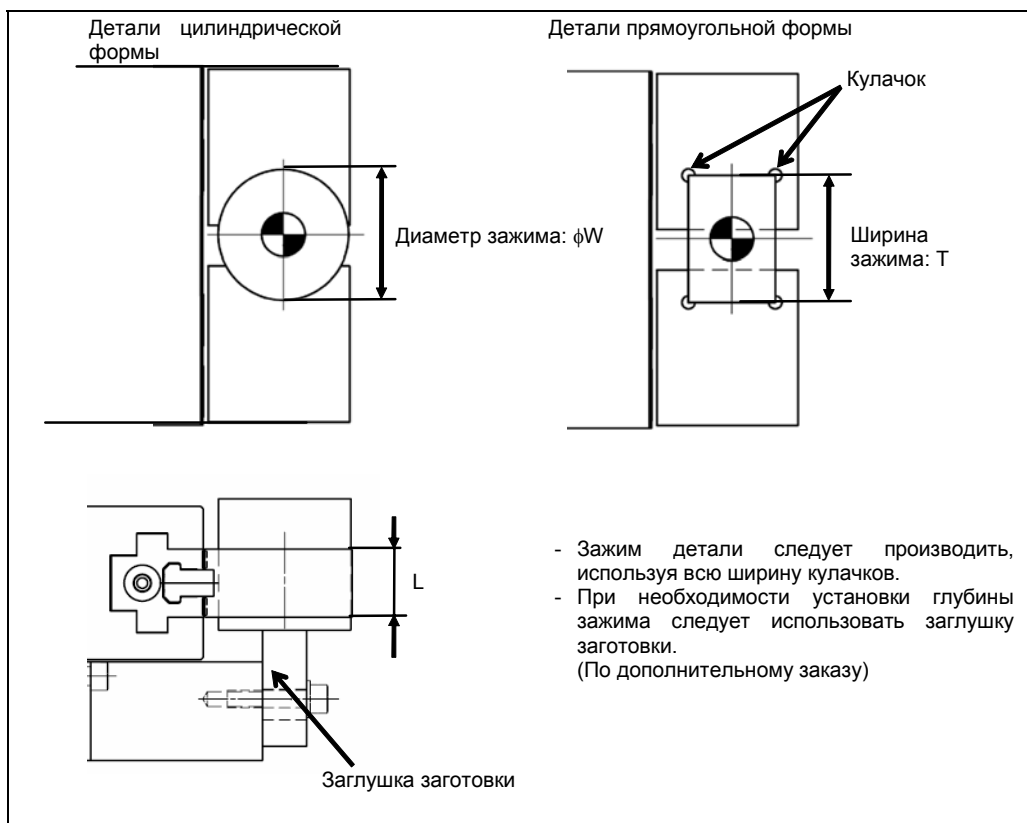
Обработка мягких кулачков (зажим заготовки по наружному диаметру 1)
